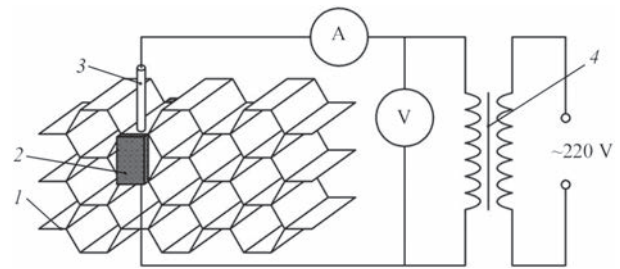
Схема устройства для сварки сотового заполнителя из сплава Ni–Cr: 1 — профилированные ленты; 2 — электрод из графита; 3 — электрод из меди; 4 — трансформатор
